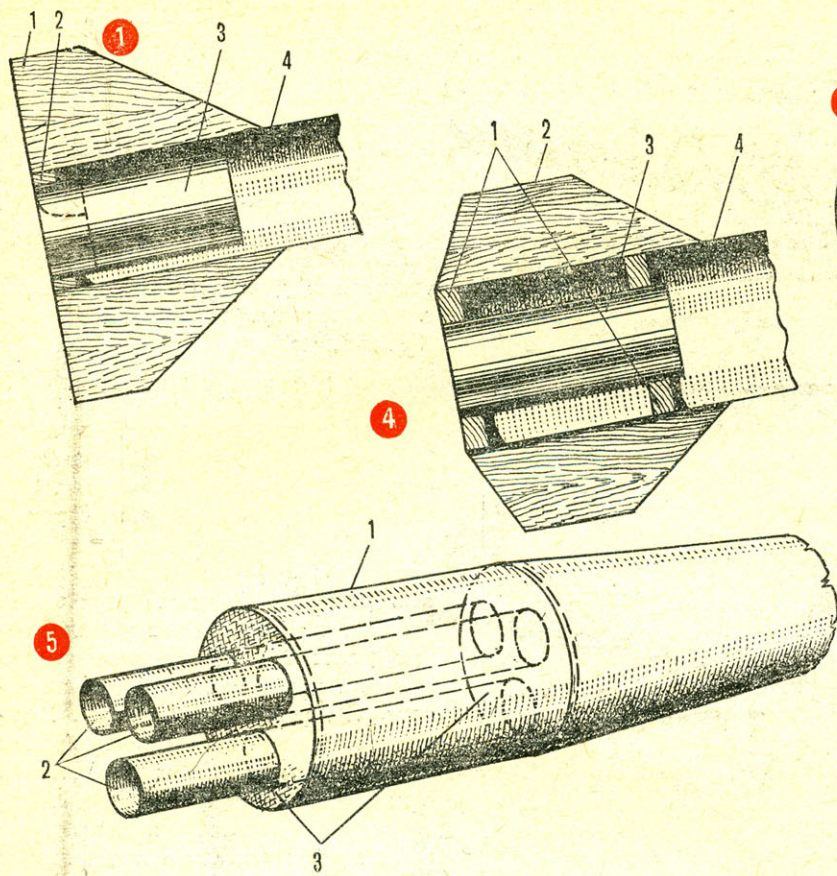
Крепление двигателя через обойму: 1 — стабилизатор, 2 — обойма, 3 — двигатель, 4 — корпус.
